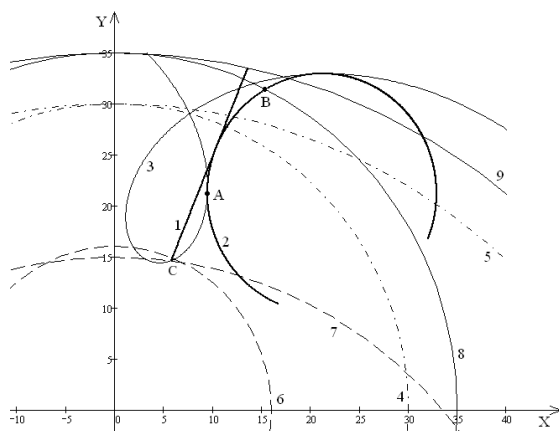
Кривые, представляющие профили зубьев колес и шестерни: отрезок 1 — правый профиль зуба колеса; дуга АВ — левый профиль зуба шестерни; дуга 2 — огибающая, образующая сопряженный профиль шестерни; петля 3 — траектория движения вершины профиля зуба колеса при обкате; окружность 4 — делительная окружность для шестерни, окружность 5 — делительная окружность для колеса; окружность 6 — окружность впадин для шестерни; окружность 7 — окружность впадин для колеса; окружность 8 — окружность вершин для шестерни, окружность 9 — окружность вершин для колеса
